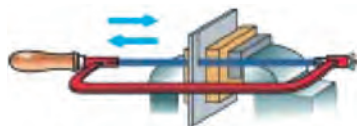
Длинные заготовки разрезают повернув полотно на 90°.
